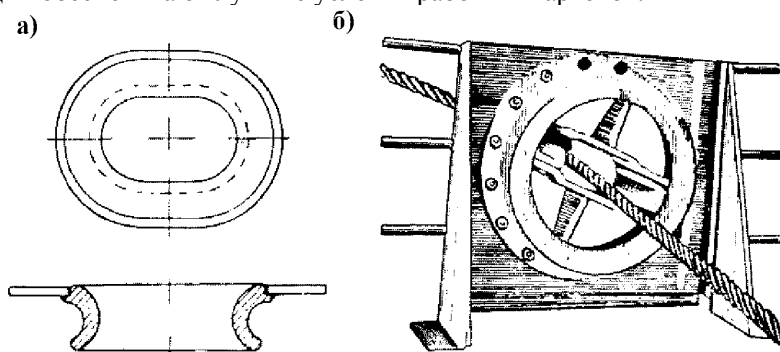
Швартовные клюзы: а – стальной литой, б – с поворотной обоймой и роульсами
